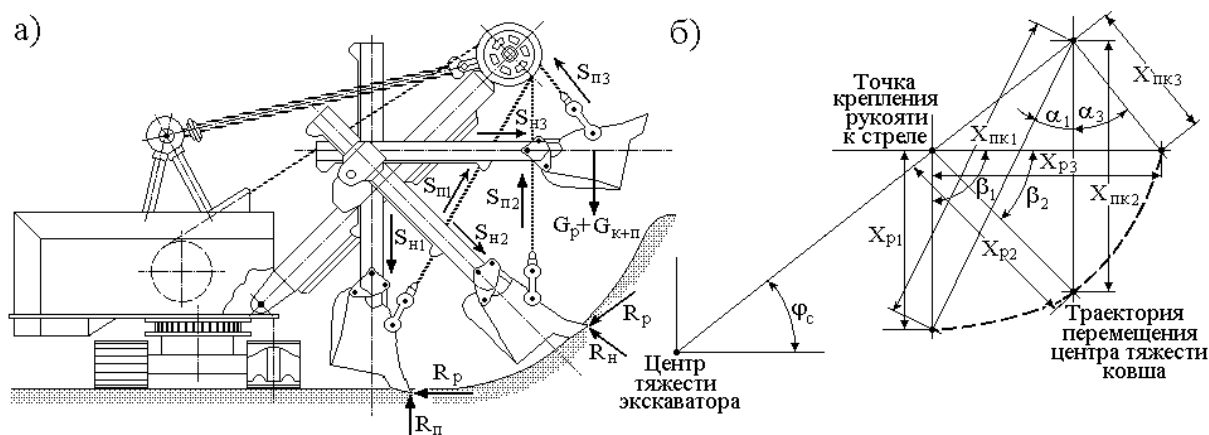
Схема положений и усилий рабочего оборудования экскаватора (а)
